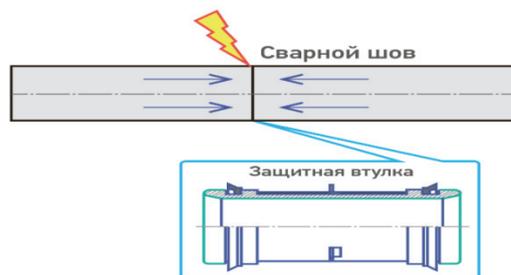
Герметизирующая втулка в трубе с внутренним изоляционным покрытием
